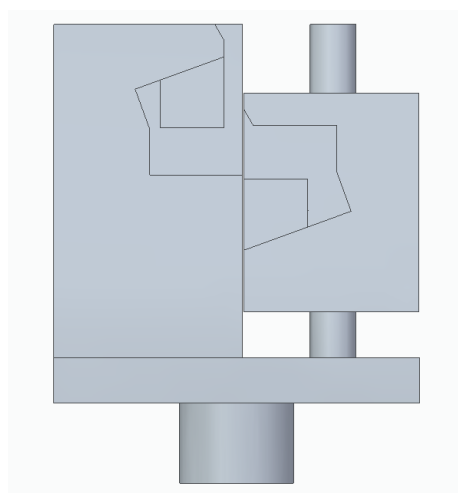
Primer diseño del utillaje para ensayo de Iosipescu
